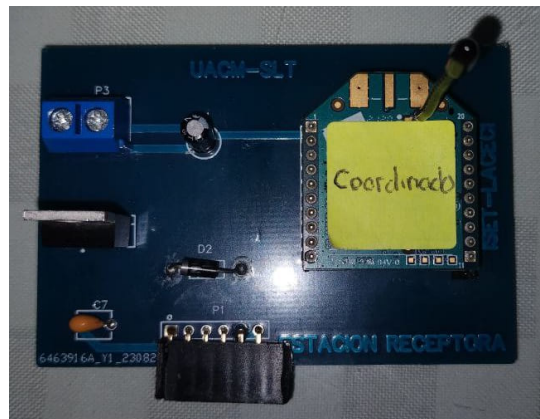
Placa receptora con sus componentes soldados
